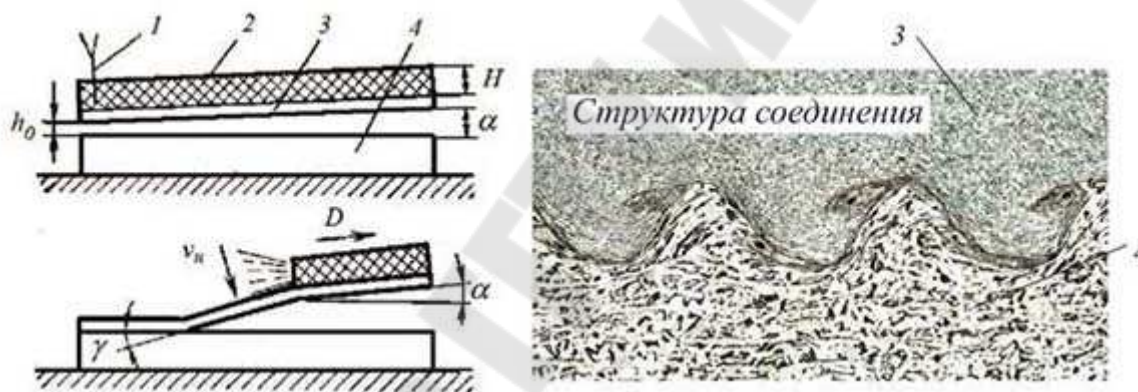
Схема сварки взрывом: 1 — детонатор; 2 — взрывчатое вещество; 3 — привариваемая пластина; 4 — заготовка
